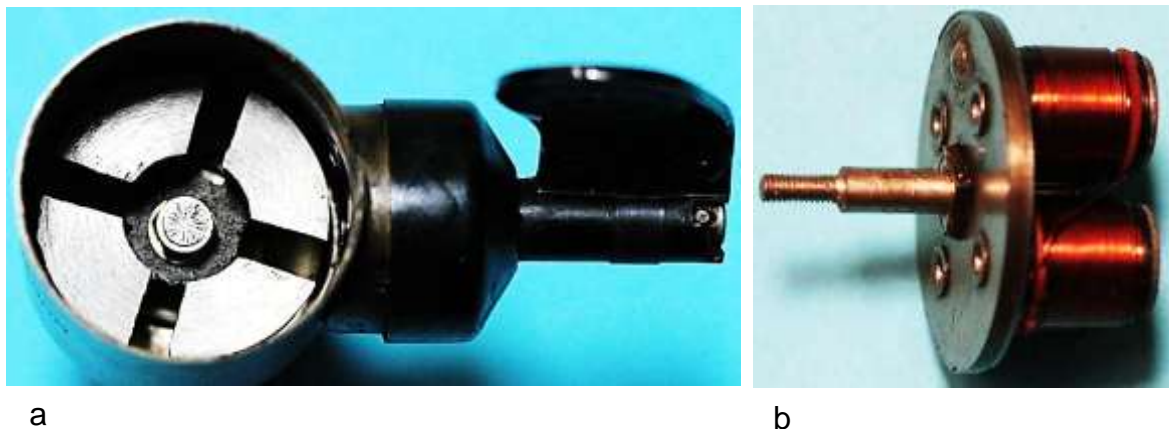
Baugruppen des Generators: a) Vierpoliger Säulenmagnet, b) Anker mit vier Spulen
